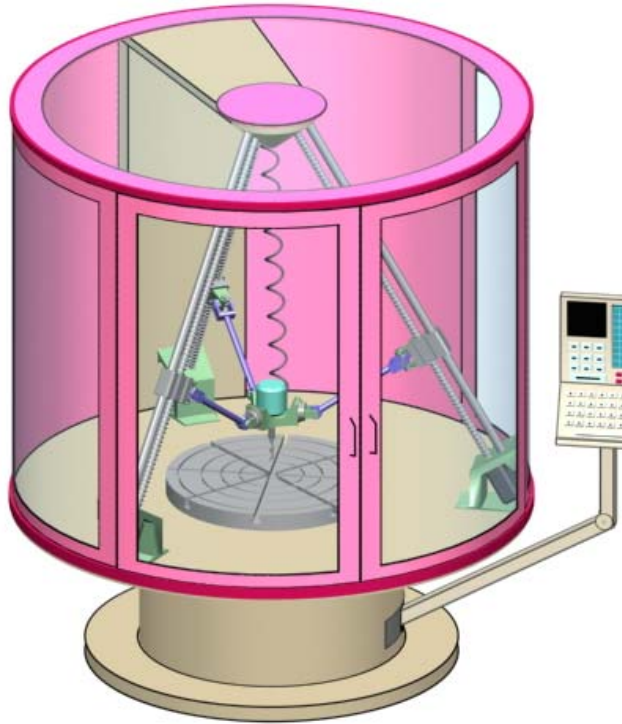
Многокоординатный сверлильно-фрезерный станок повышенной жесткости
